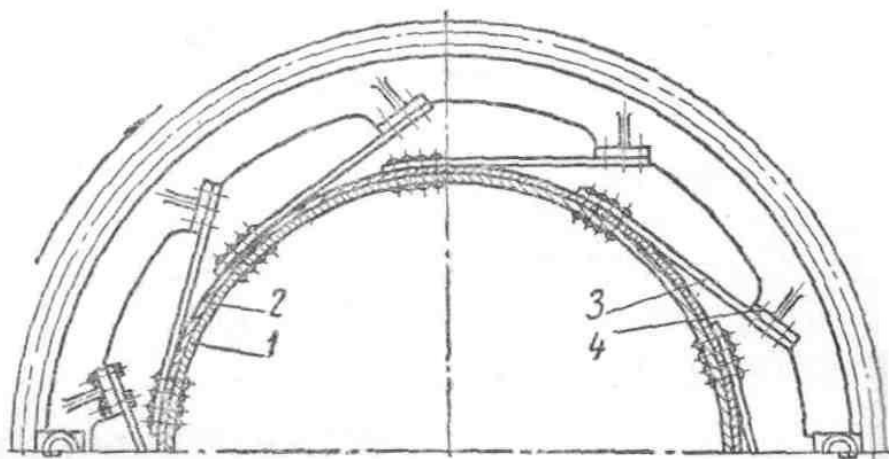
Кріплення вінцевої шестерні до барабана тангенціальними пружинами: 1 – барабан; 2 – пояс жорсткості; 3 – плоска пружина; 4 – лапа шестерні
